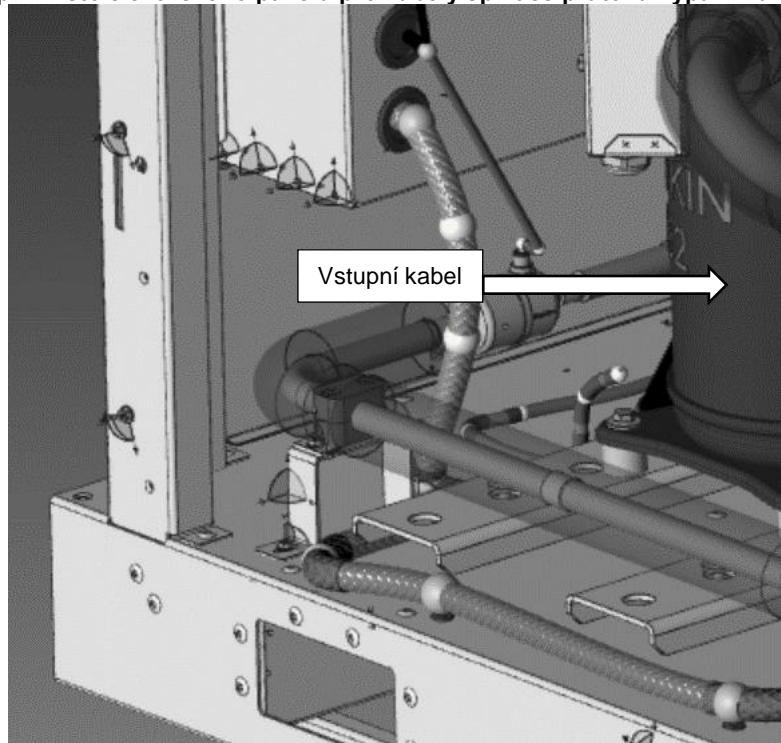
Vedení kabelů spínače průtoku výparníku
